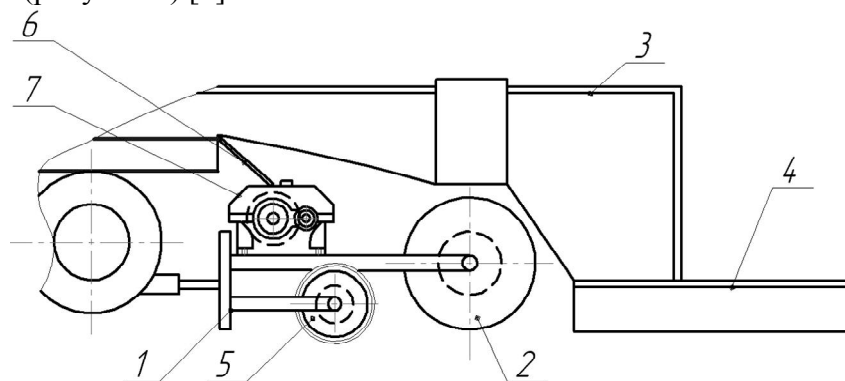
Конструктивная схема катка-ложеобразователя машины для уборки лука: 1 – рама; 2 – валец цилиндрический; 3 – лоток сужающий; 4 – образователь валка; 5 – валец спиральный; 6 – лоток схода примесей; 7 – гидравлический двигатель.
